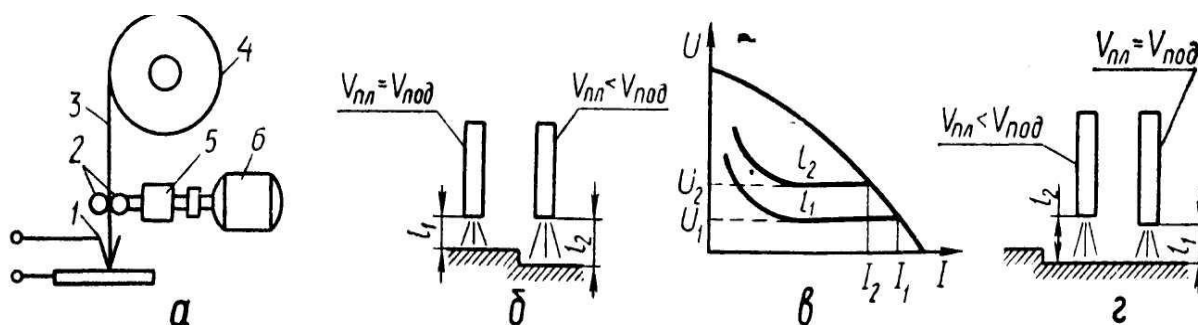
Схемы устройства сварочного автомата и процесса саморегулирования длины дуги
